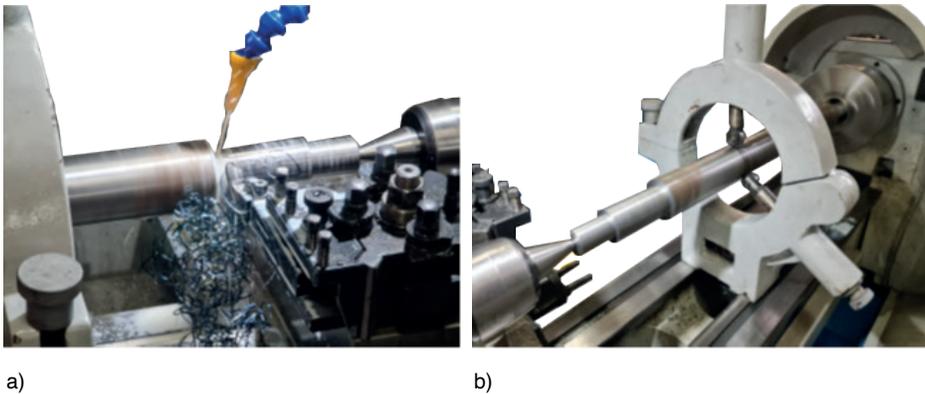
Proceso de torneado de los rodillos de rolado de la máquina. a) cilindrado de rodillo, b) etapa final del proceso de torneado del rodillo
